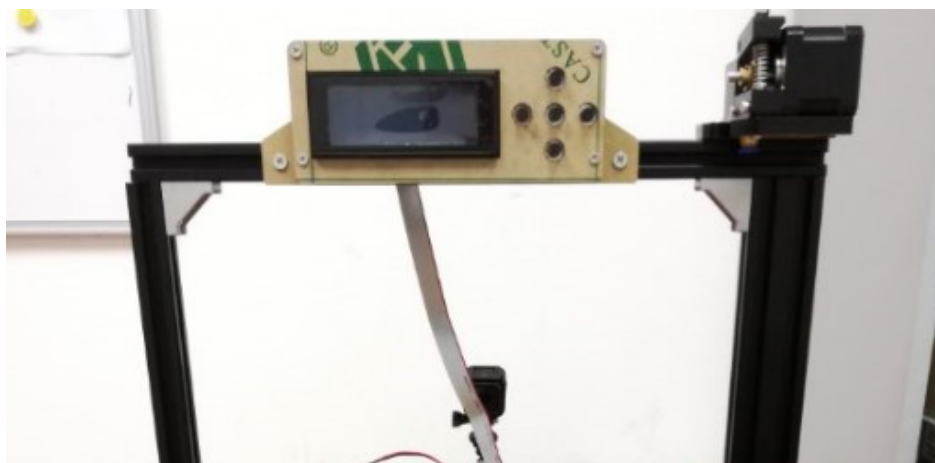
Nainstalovaný řemen extruderu
